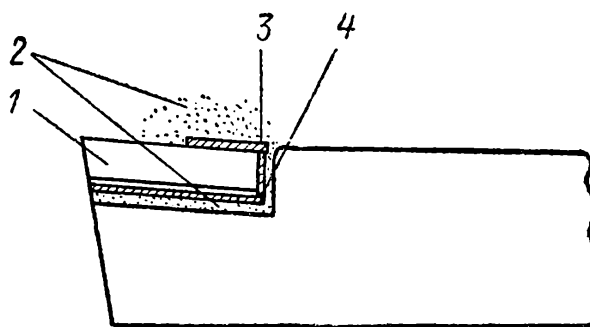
Схема напайки пластинки на державку резца на высокочастотной установке.
